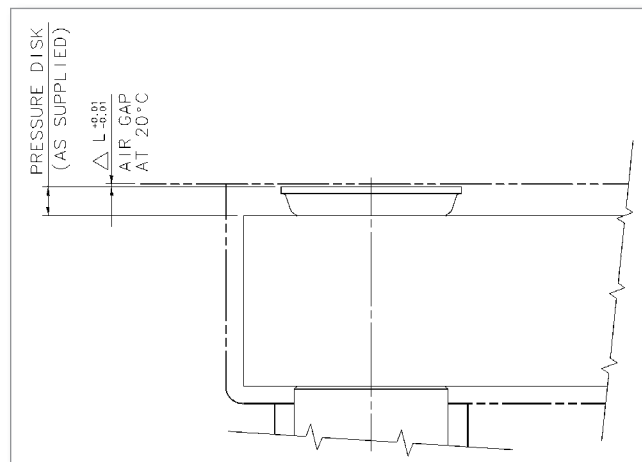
Detalhe de montagem do disco de pressão opcional
